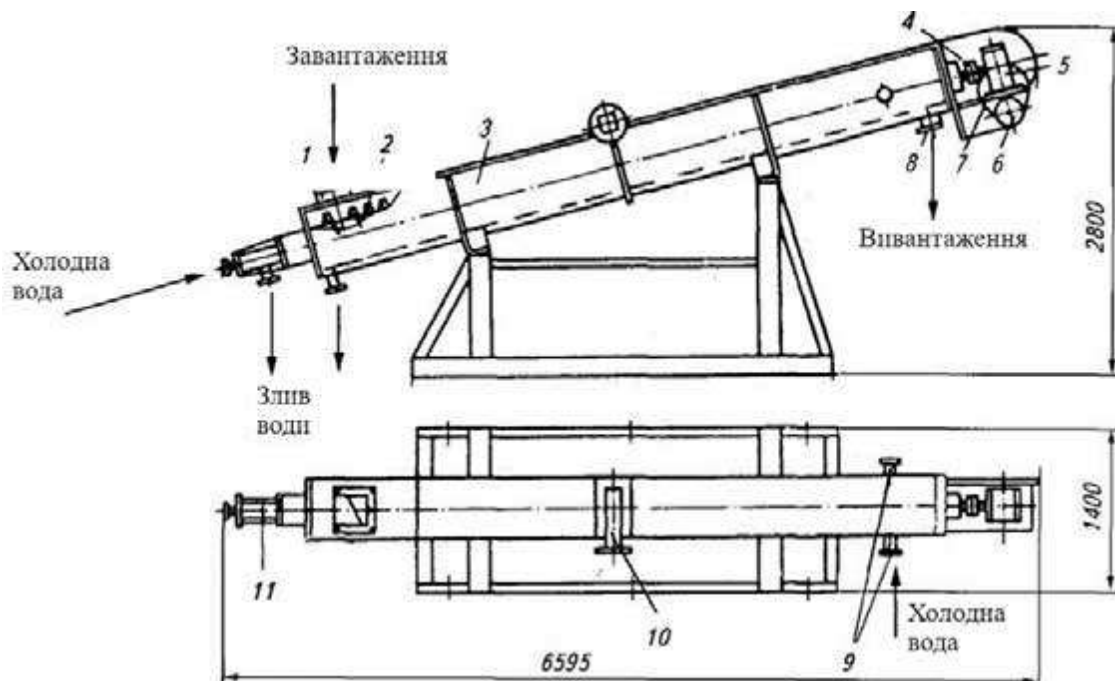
Шнековий охолоджувач для шквари: 1, 8 – горловини завантаження і вивантаження; 2 – шнек; 3 – корпус; 4 – муфта; 5 – черв'ячний редуктор; 6 – електродвигун; 7 – ланцюгова передача; 9 – патрубки для подачі холодної води; 10 – патрубок для видалення пари; 11 – вузол для подачі води у шнек
